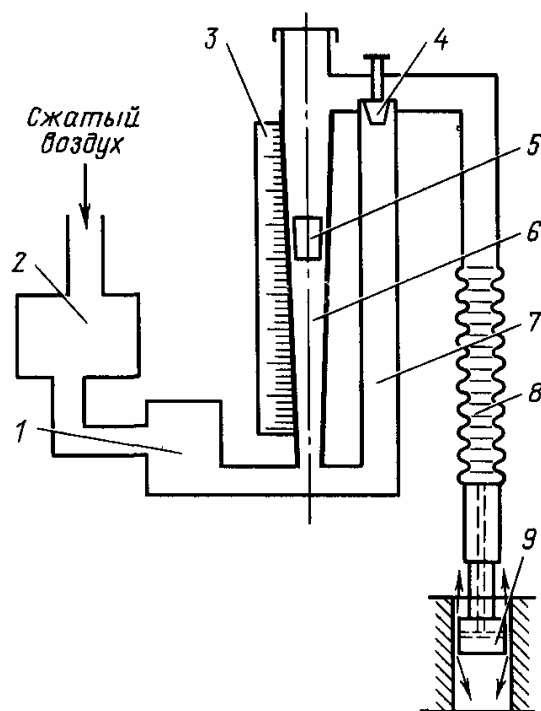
Схема пневматического измерительного стенда: 1 – стабилизатор давления; 2 – влагоотделитель; 3 – шкала; 4 – кран; 5 – поплавок; 6 – стеклянная коническая трубка; 7 – обводная трубка; 8 – гофрированный шланг; 9 – пневматический калибр
